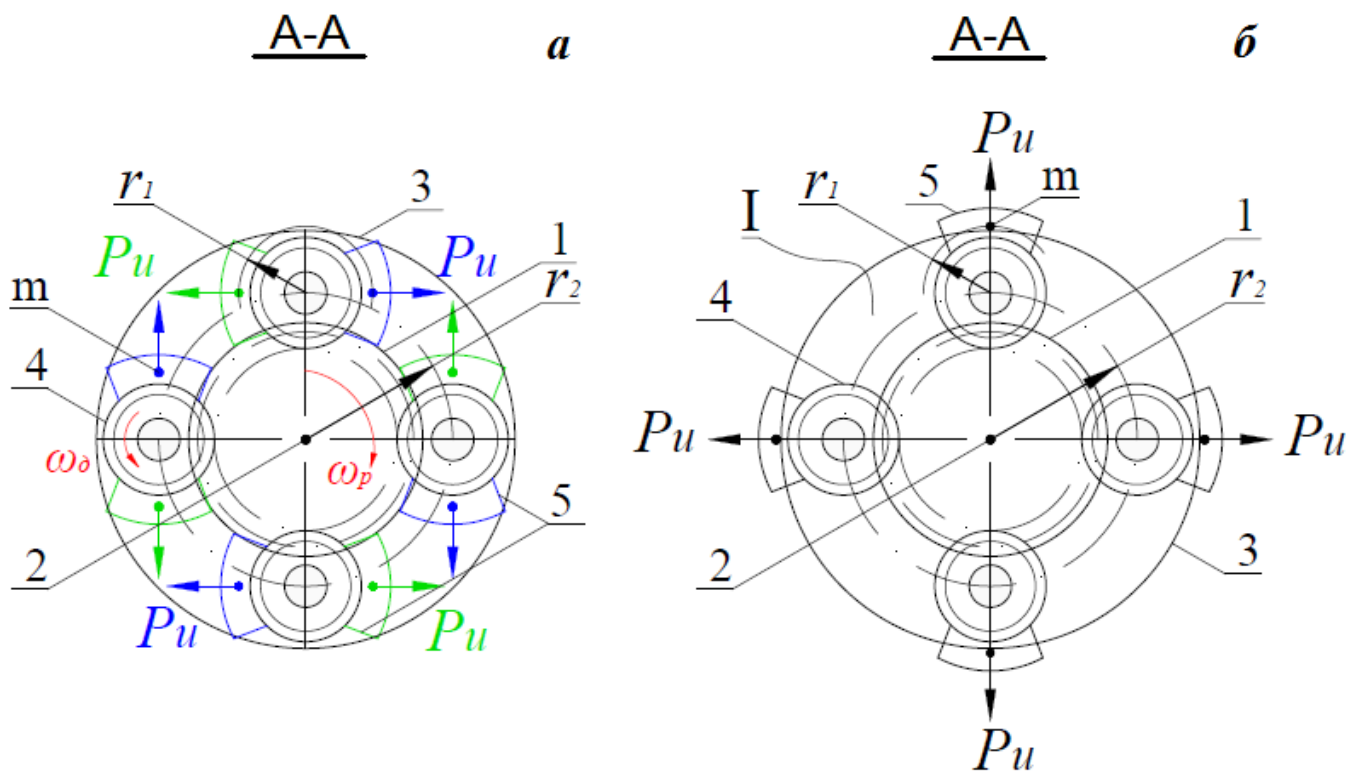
Принципиальная кинематическая схема центробежного генератора гармонических колебаний движущего момента конструкции МГГУ (сечение А-А рисунка 3.7 б) при: работающем – а и обесточенном дополнительном электродвигателе – Дс – б.
